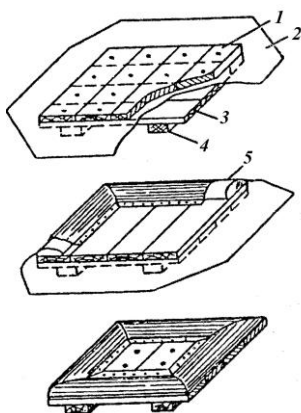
Изготовление деревянного пластыря с мягкими бортами:
